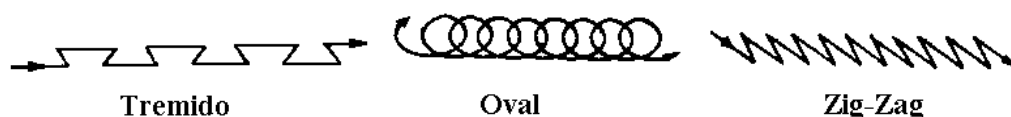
Movimentos típicos de eletrodo na soldagem sobre cabeça
